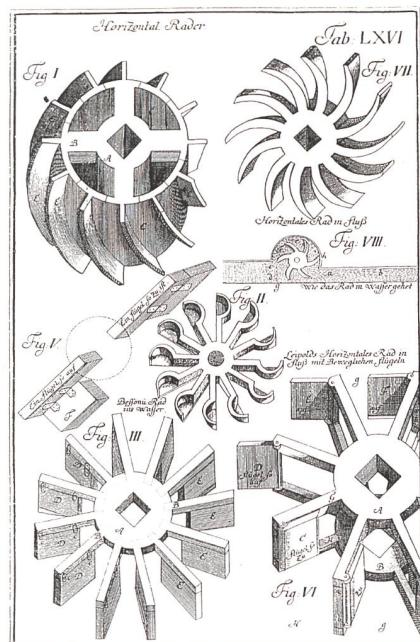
Einige Wasserräder aus früheren Jahrhunderten/Avant les turbines: roues hydrauliques
